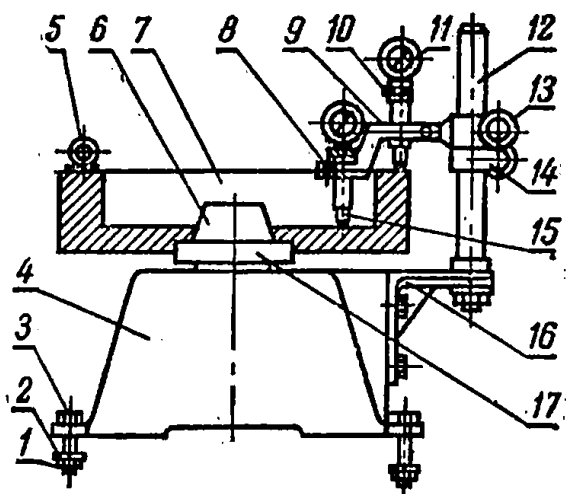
Приспособление для контроля маховика двигателя СМД-14:
